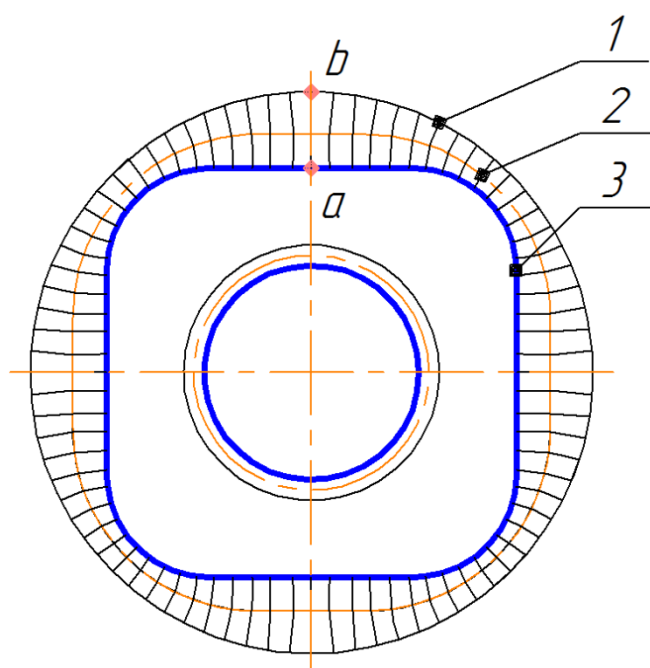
Контуры поперечного сечения заготовки (1), готовой трубы (3) и промежуточного перехода (2).
